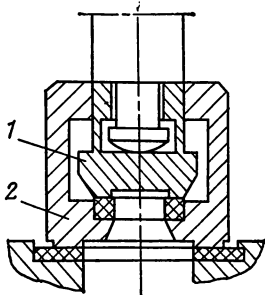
Запорный клапан с внутренней загрузкой:
